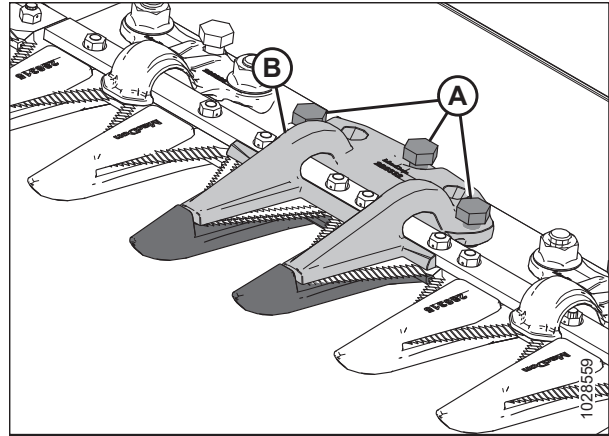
Загострений центральний протиріжучий палець ножа
